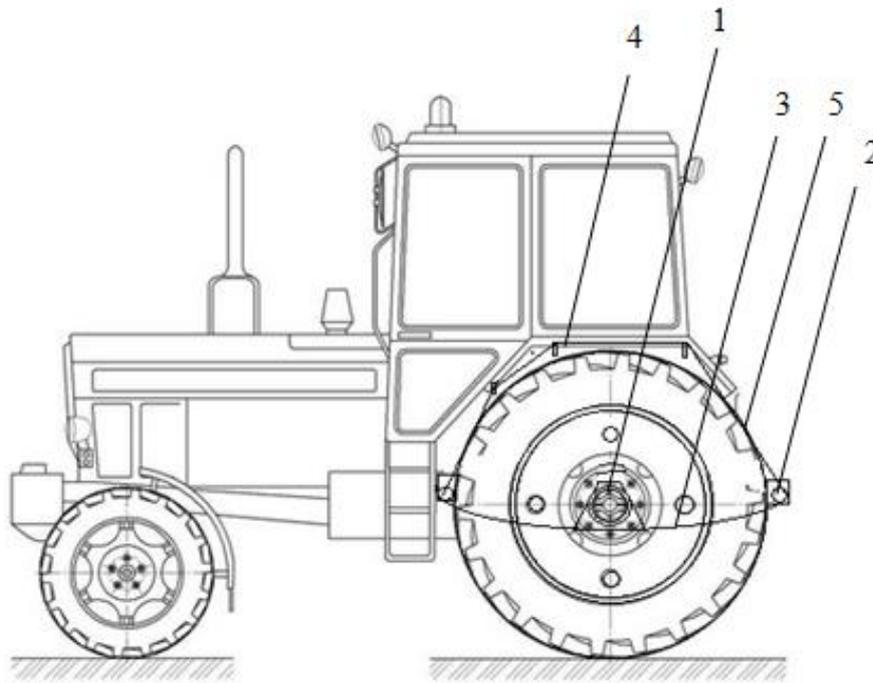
Стабилизатор высоты протектора движителя трактора (1-косыночный упор с подшипником, 2 - болтовой фиксатор с ограничителем, 3 – плоская пружина рессорного типа, 4-крюковые ограничители, 5-гибкая цепная связь)
